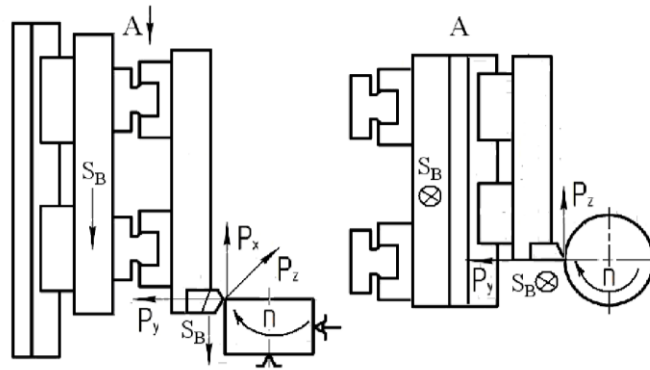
Робоча зона токарного верстата із ЧПК та схематичне зображення проєкцій сил різання на супорт під час токарної обробки із подачою  $S_{пр}$
